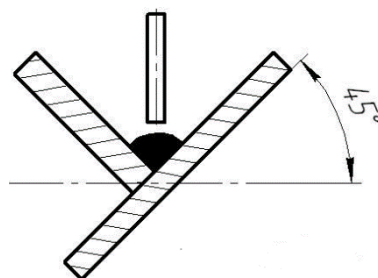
Сварка угловых швов положения в «лодочку»
